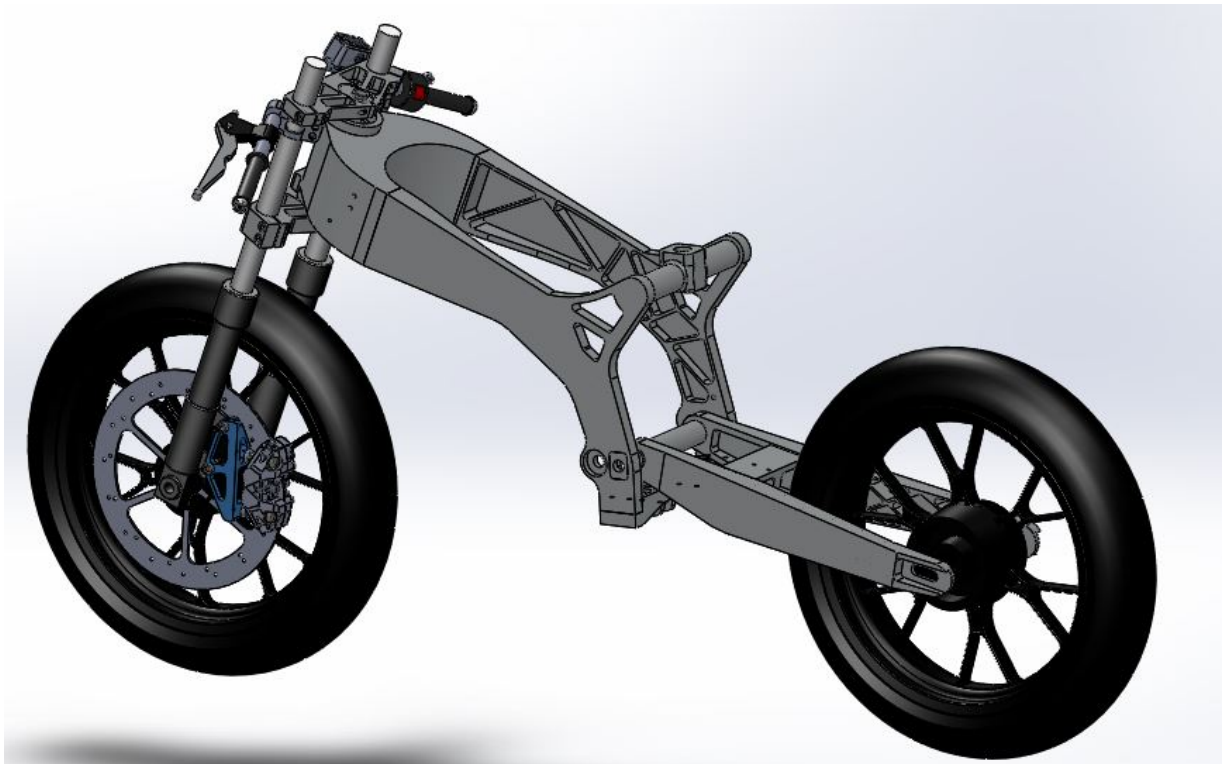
Fabricación. Ensamblaje. Vista general.
